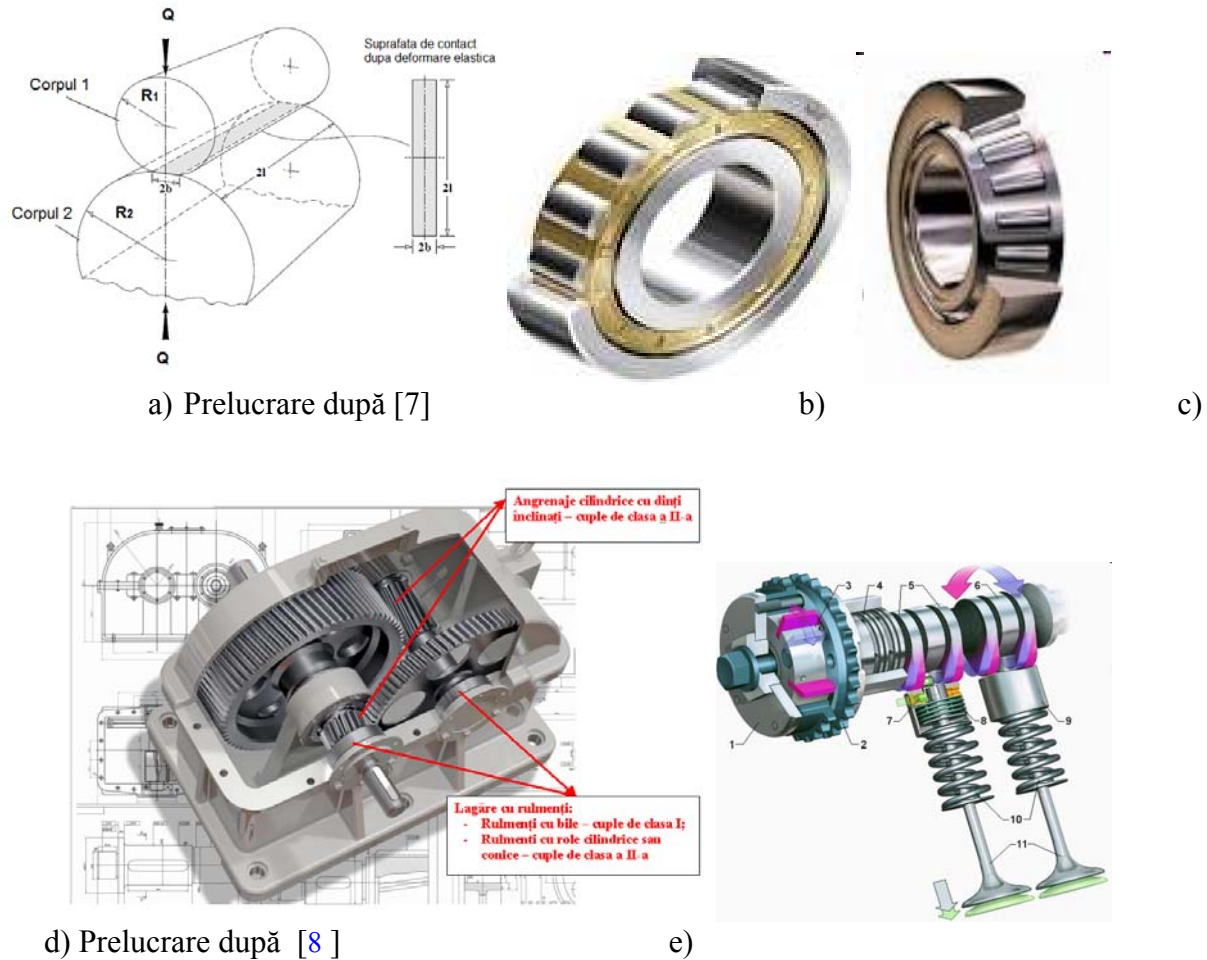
Cuple de frecare de clasa a II-a : contactul a doi cilindri cu evidențierea suprafeței de contact - a), rulmenți radiali cu role cilindrice - b), rulmenți radial-axiali cu role conice - c), reductor roți dințate – d), mecanisme camă - tachet – e)
